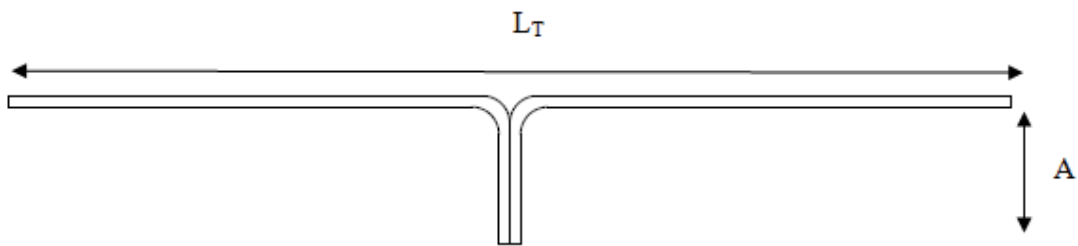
Dimension des éprouvettes soudées.
